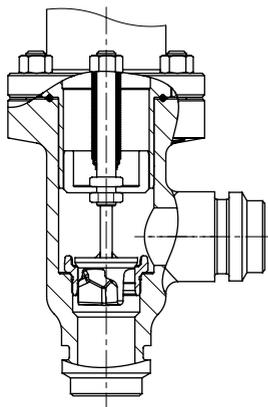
Угловой клапан в алюминиевом корпусе Тип 3248
